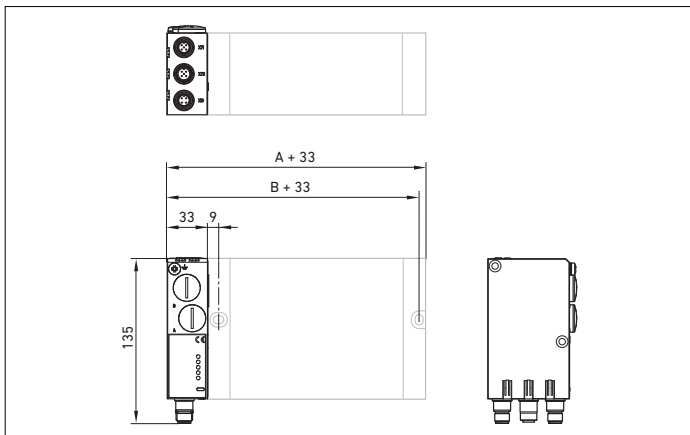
Disegno quotato del sistema di valvole (accoppiatore bus e valvole)
